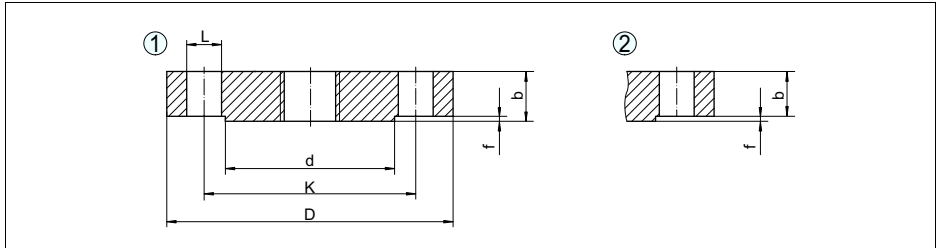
Maße - JIS-Flansch (Regular Flange)
